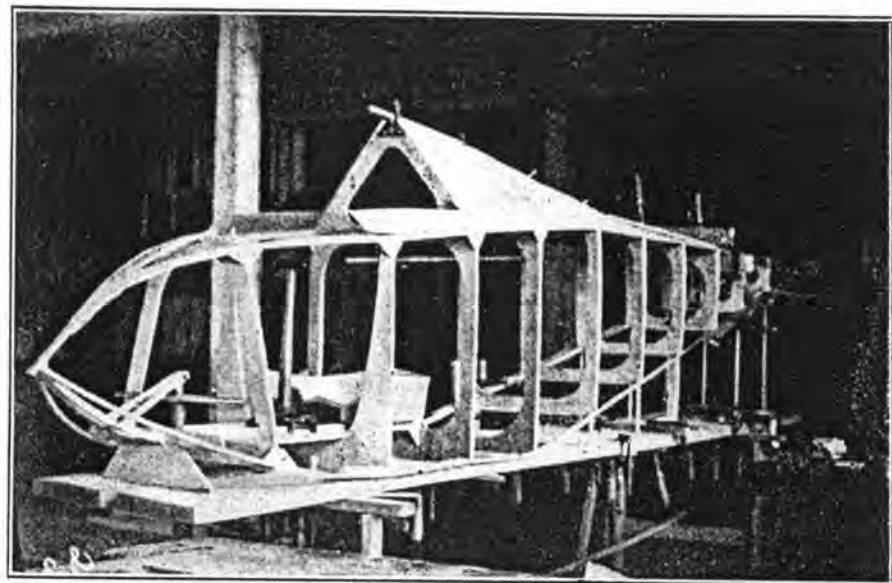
Sperrholzrumpf auf der Helling. Darmstadt-Eindecker „Edith“. Dachförmiger Rumpfaufbau schon mit Sperrholz beplankt.
